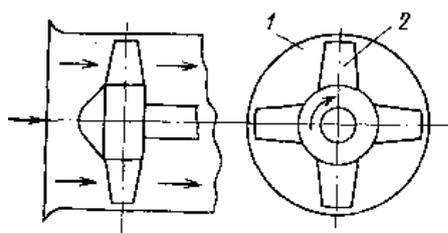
Осевой (пропеллерный) вентилятор: 1 – корпус; 2 – рабочее колесо
